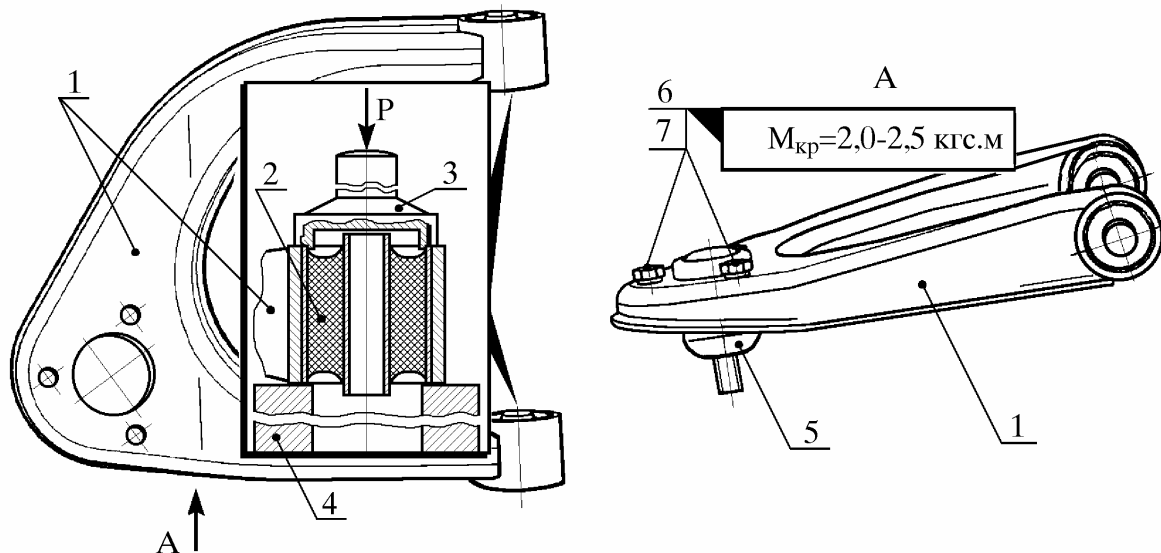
Запрессовка сайлентблоков и установка верхнего шарнира левого (правого) в отверстия верхнего рычага:
